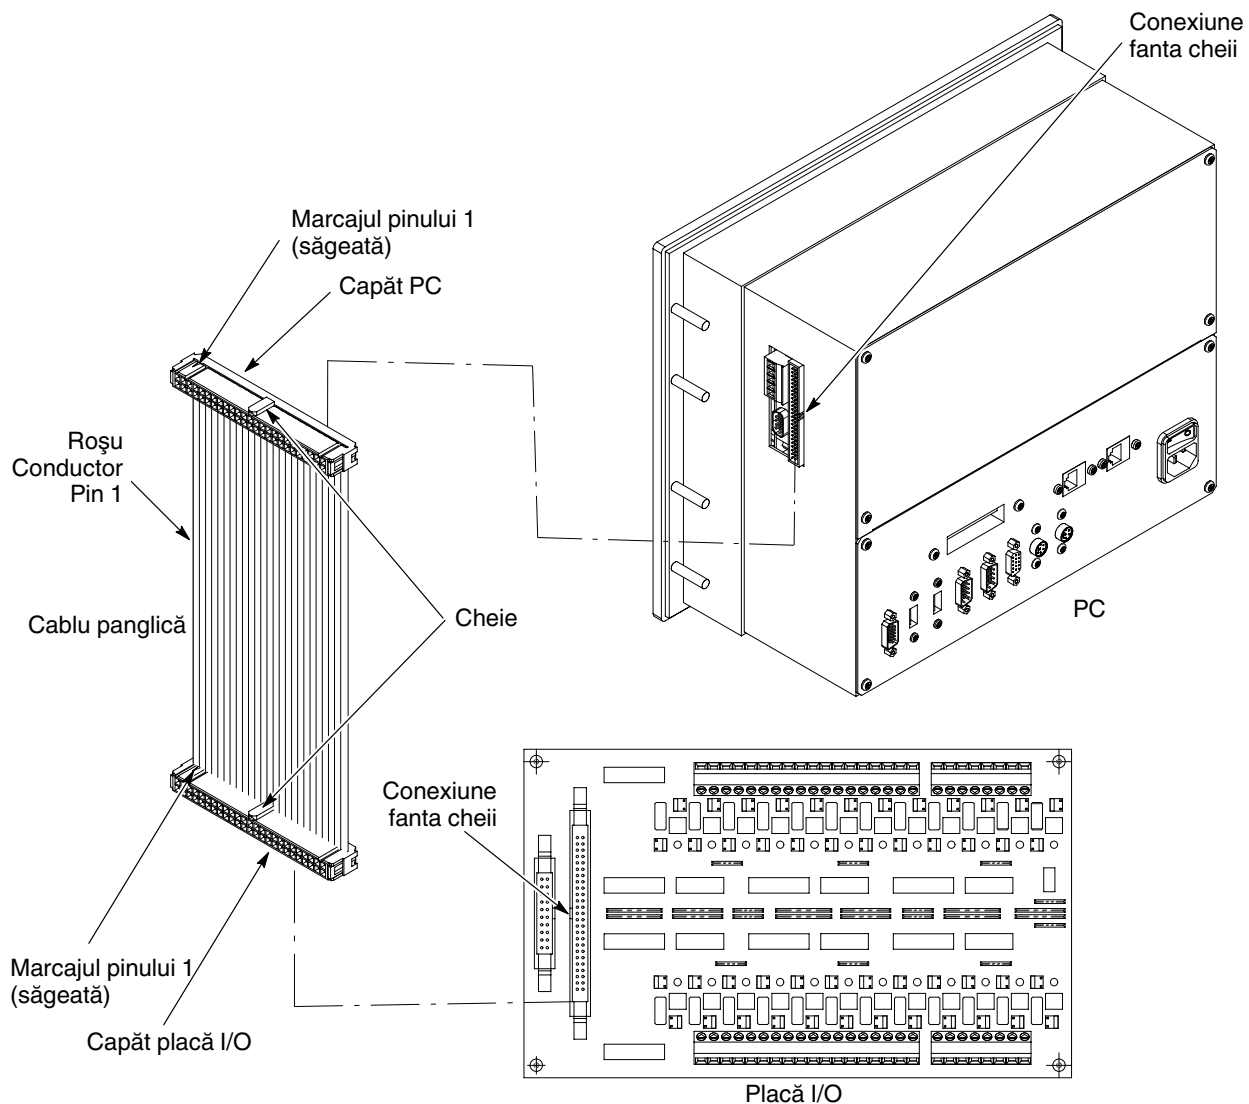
Conexiunile cablului panglică al plăcii I/O PC
